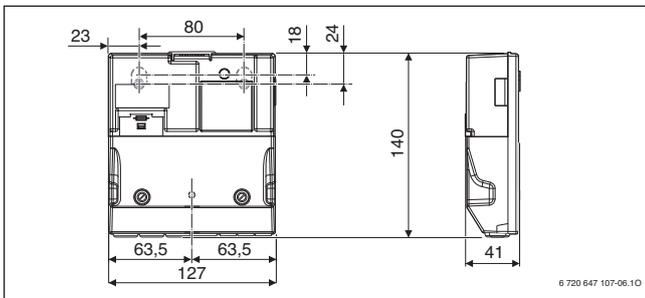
Abmessungen Heizkreismodul MM50 bei Installation an der Wand (Maße in mm)
